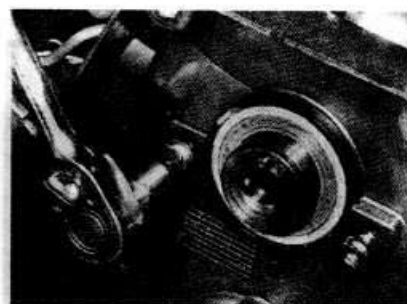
Отворачивание верхнего винта задней крышки ремня — двигатель 1,6 л с многоточечным впрыском топлива
